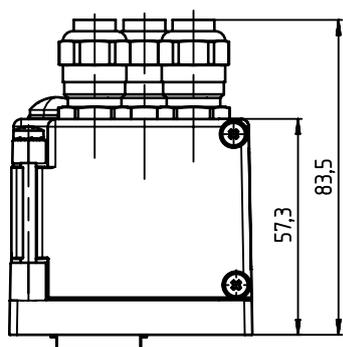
Desenho dimensional BPS com tampa de conexão ME 348
